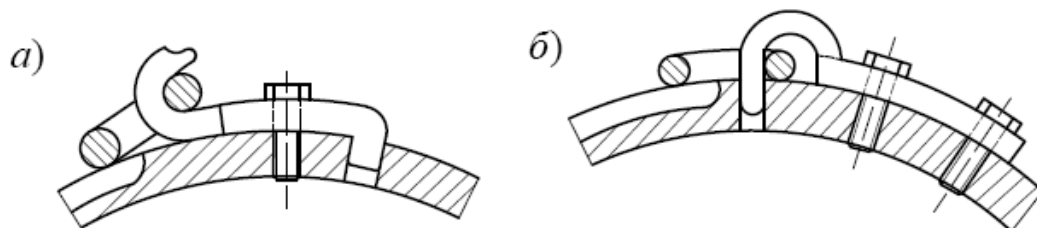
Крепление сварной цепи к барабану:
